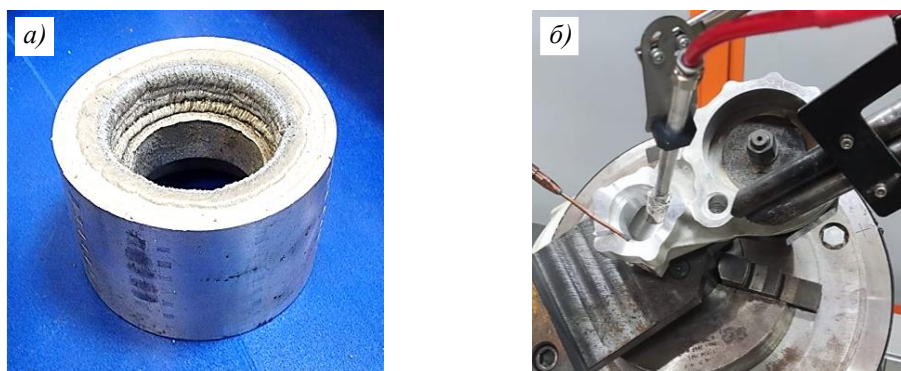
Внешний вид деталей «Втулка» (а) после ремонта внутренней цилиндрической поверхности и «Корпус компрессорного агрегата» (б) из алюминиевого сплава АД33
